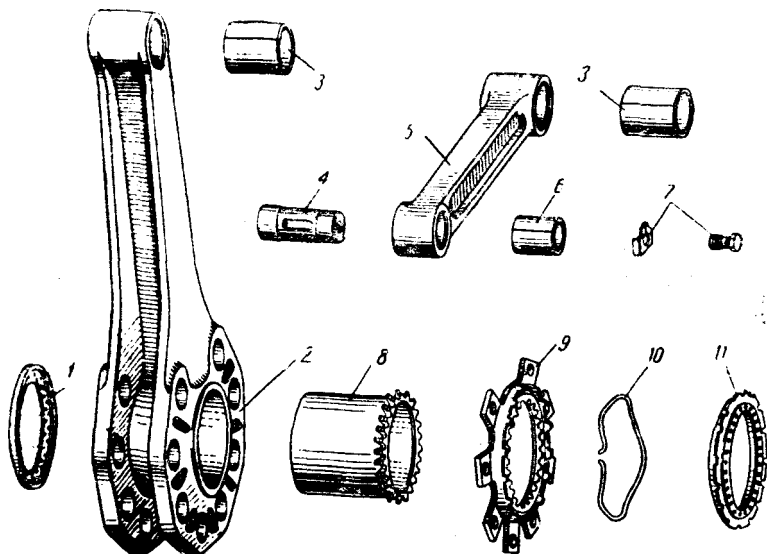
Шатунный механизм: 1—заднее кольцо главного шатуна; 2—главный шатун; 3—втулка поршневой головки; 4—палец прицепного шатуна; 5—прицепной шатун; 6—втулка кривошипной головки прицепного шатуна; 7—болт и замок для крепления замка втулки главного шатуна; 8—втулка главного шатуна; 9—замок втулки главного шатуна
